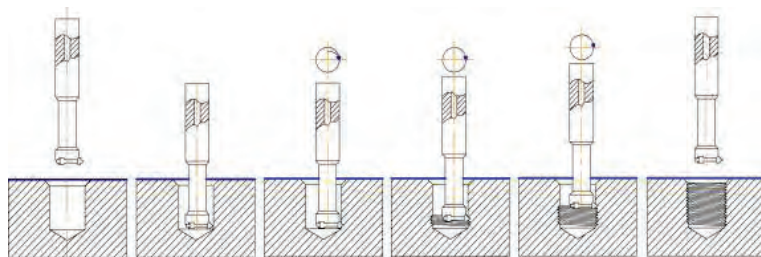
Схема нарезания резьбового отверстия на станке с ЧПУ односторонней фрезой
